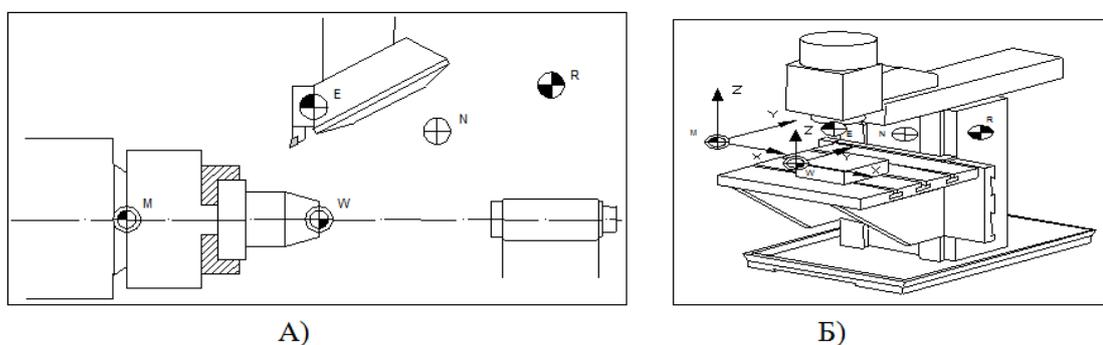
Расположение нулевых точек на токарном (А) и на вертикально-фрезерном (Б) станке с ЧПУ
